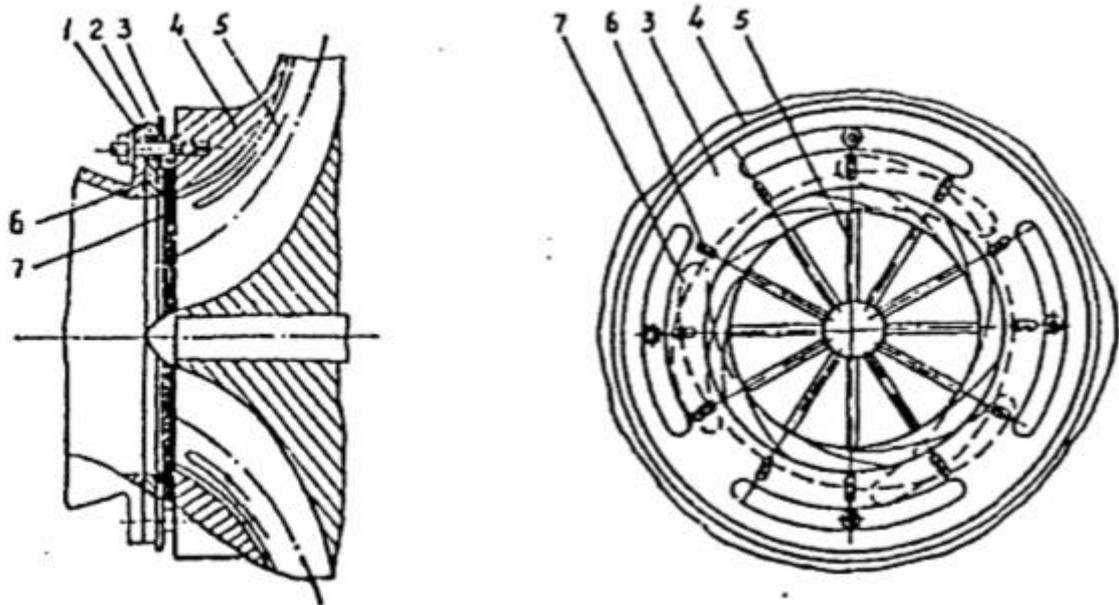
Схема устройства и установки ирисовой диафрагмы для регулирования производительности центробежного нагнетателя; 1 - входное устройство; 2 - неподвижный диск; 3 - подвижный диск; 4 - корпус нагнетателя; 5 - рабочее колесо нагнетателя; 6 - штифт лепестка; 7 - лепесток ирисовой диафрагмы
